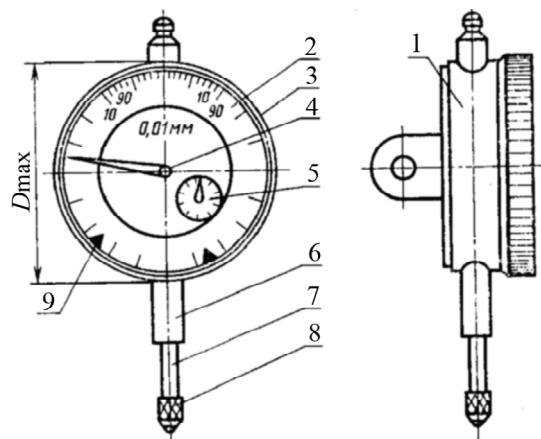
Внешний вид и основные размеры индикаторов типа ИЧ:
